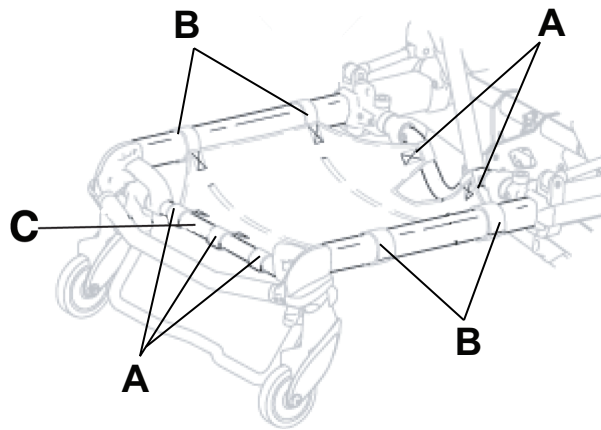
Dispositivo plano de almacenamiento del extremo de la cabeza
